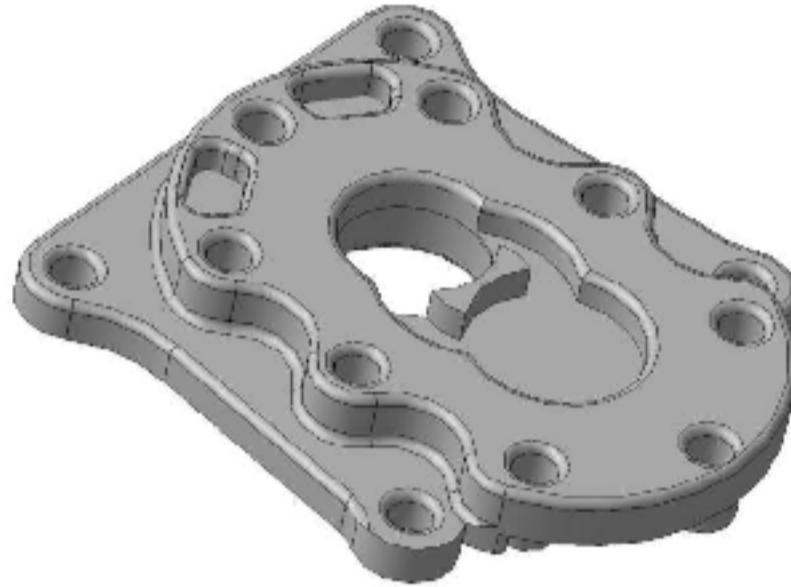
3D-модель заготовки виготовленої литтям під тиском
